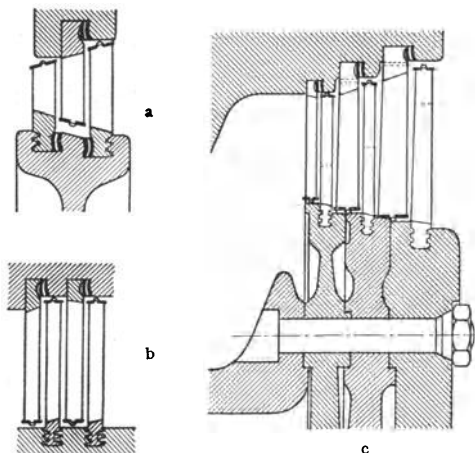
a bis c. a Curtis-Rad für Hilfsturbinen. b Ausschnitt aus Mitteldruckteil der Hauptturbine. c Niederdruckkopf der Hauptturbine.
